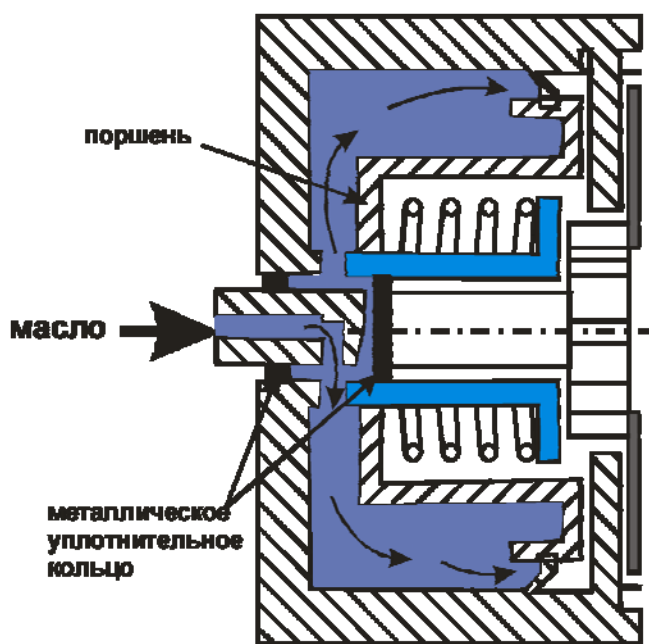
Конструктивная схема автоматической коробки передач с установкой металлических уплотнительных колец
